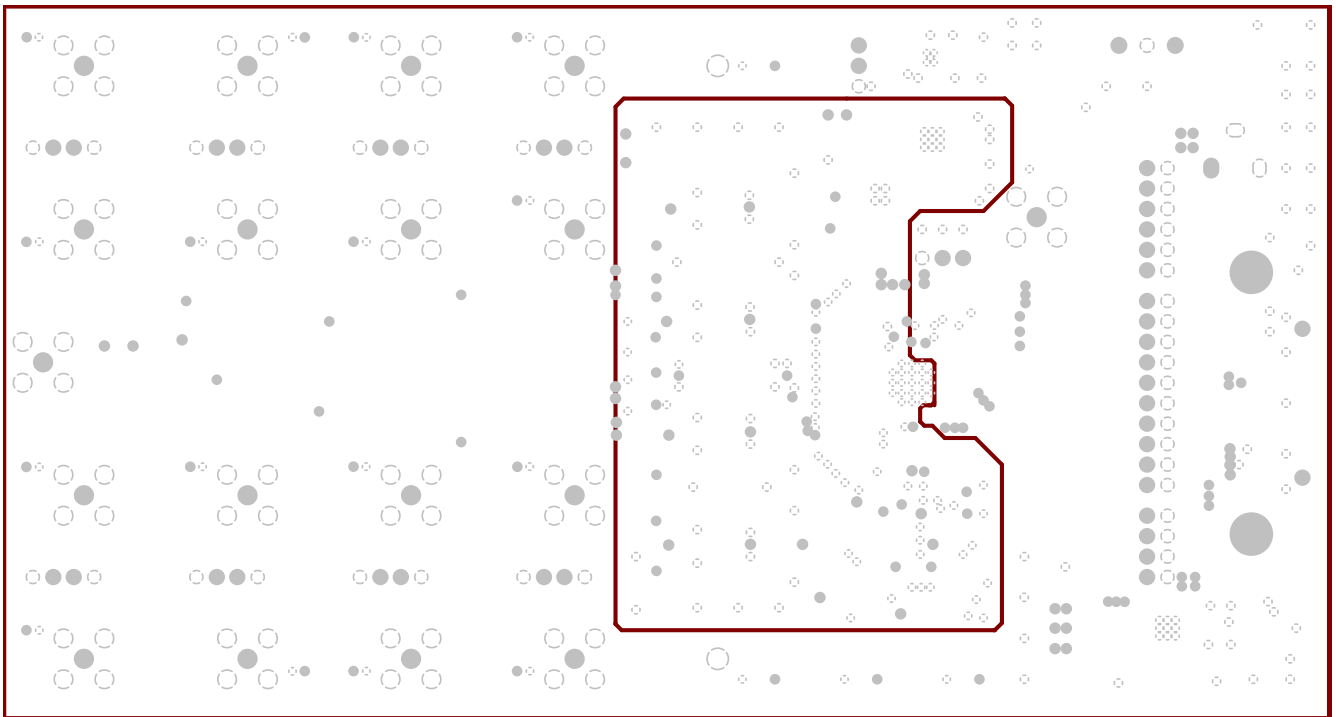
ADS127L18EVM 的 PCB 布局 (内部 AVSS/GND 平面 2)
